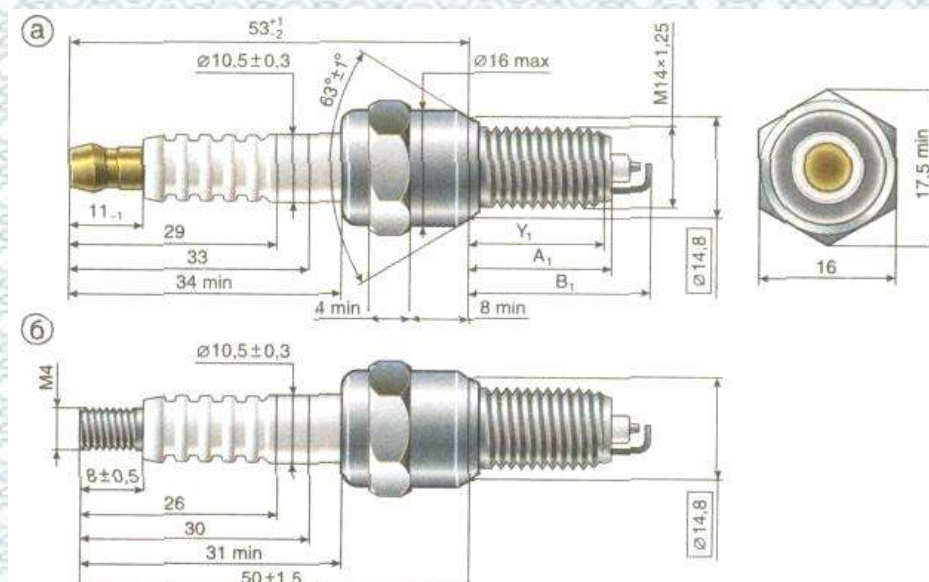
Габаритні й приєднувальні розміри свічок M14x1,25 з конічною опорною поверхнею: а - зі штировою контактною головкою; б - з різьбовою контактною головкою
